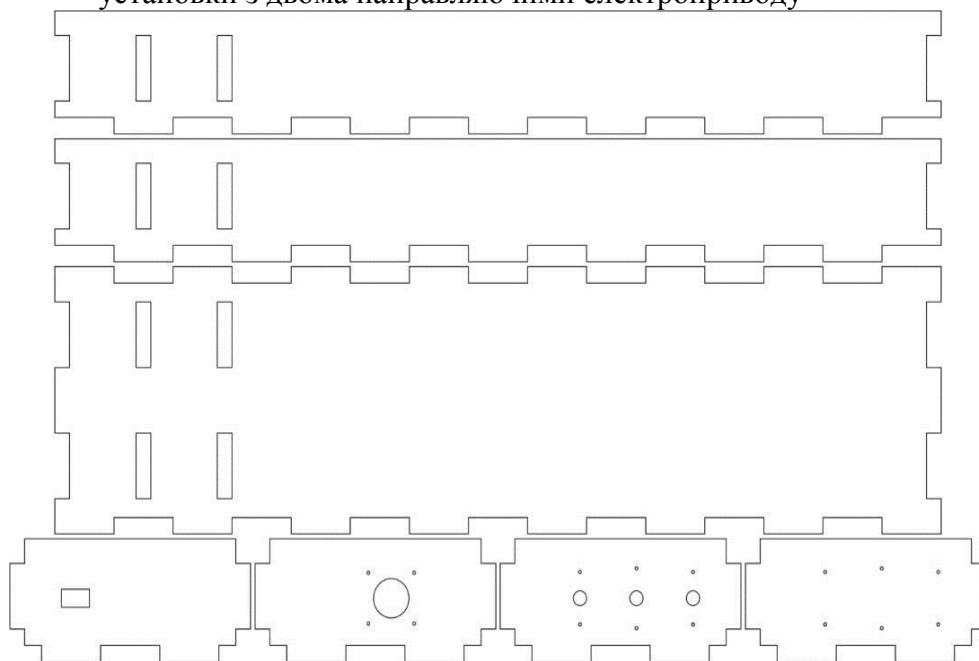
Ескізне креслення несучого корпусу рентгентелевізійної установки
